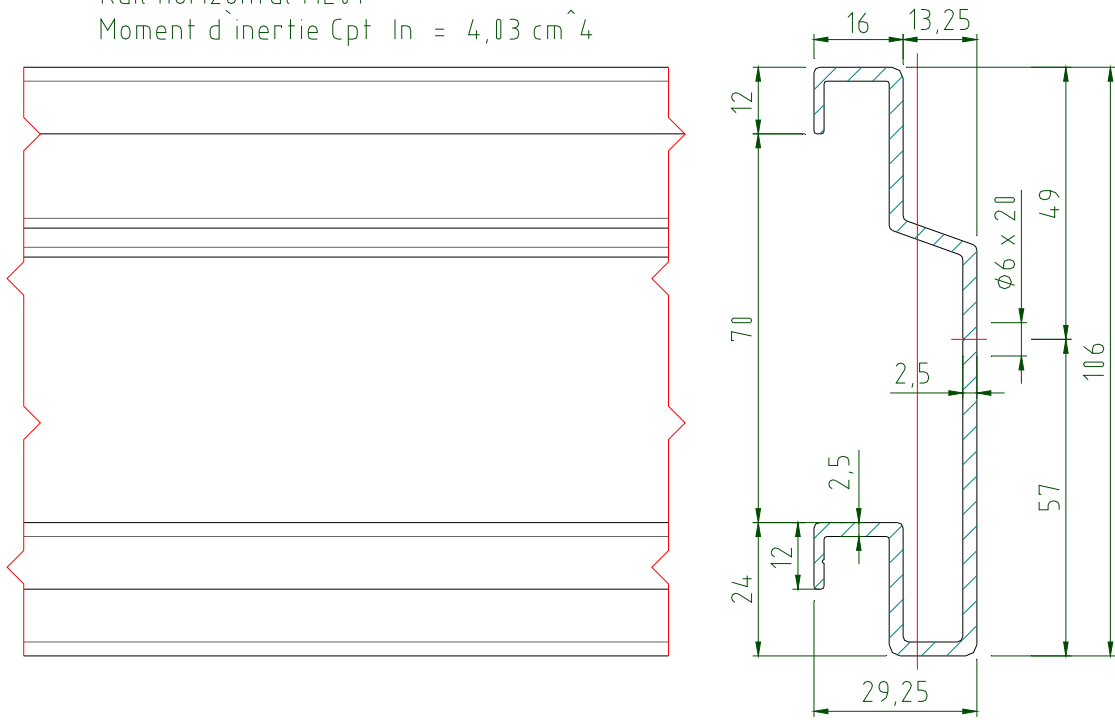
Rail horizontal aluminium épaisseur 2,5 mm (longueur maxi 3 m)
